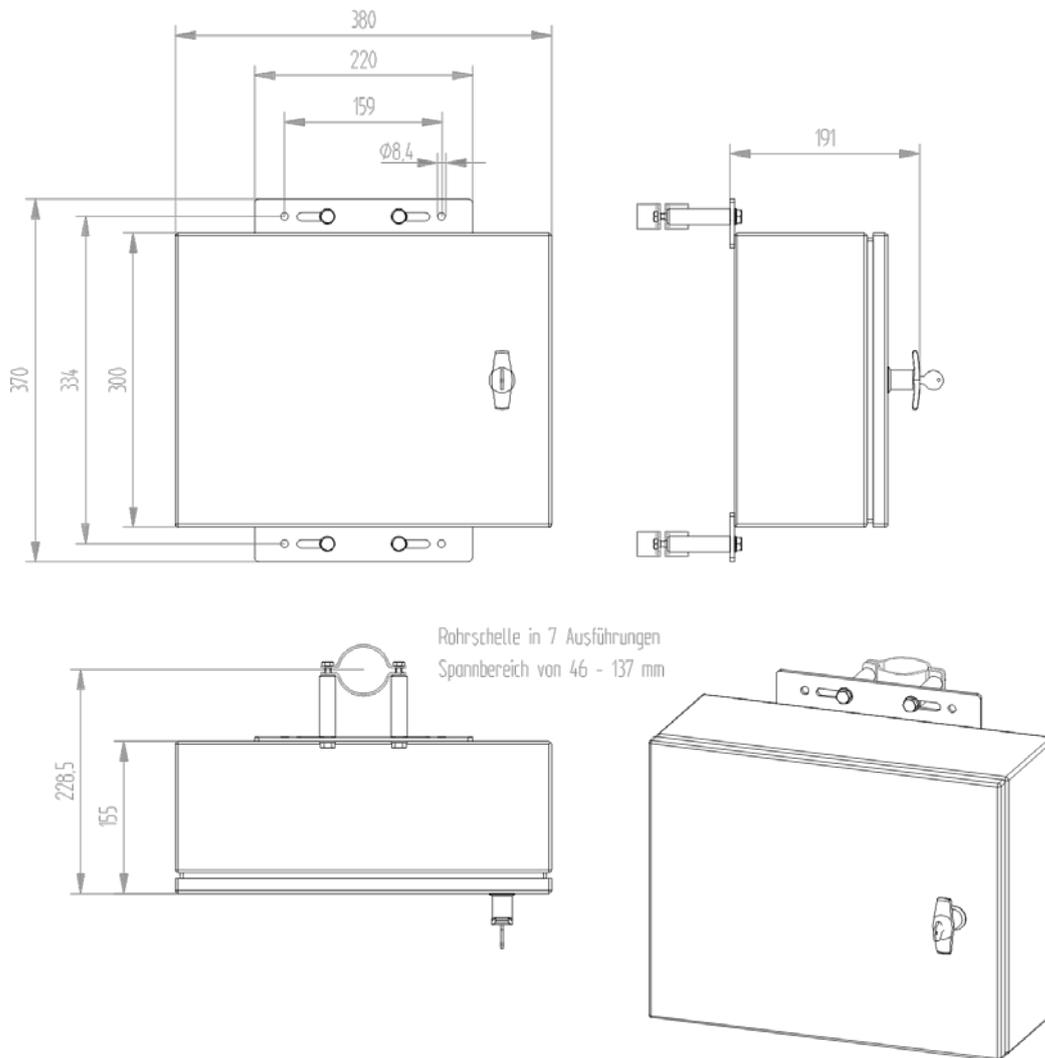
Maßzeichnung von Gehäuse-Version A (9.175x.10.x0x) (in mm)
